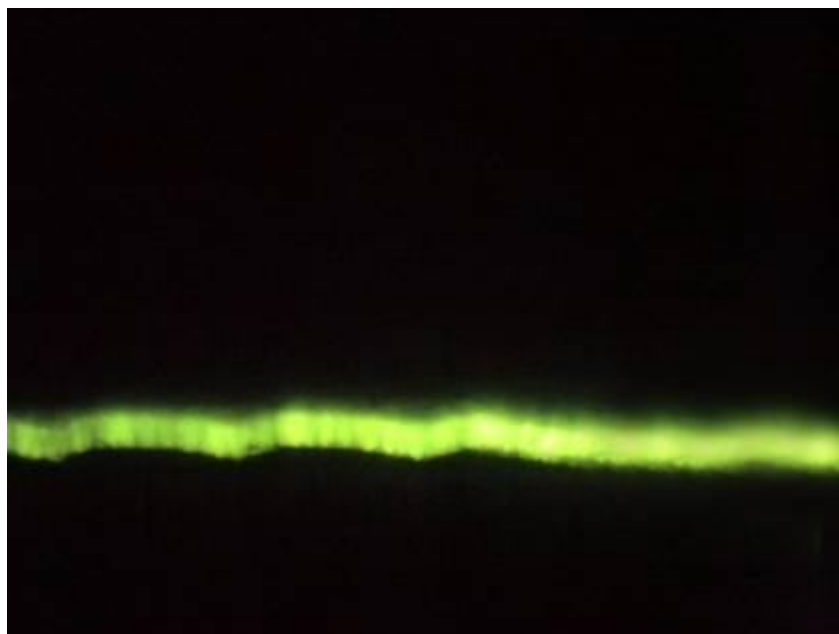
Шероховатость поверхности стали с применением СОЖ – ТМ-2 при чистовой обработке.
